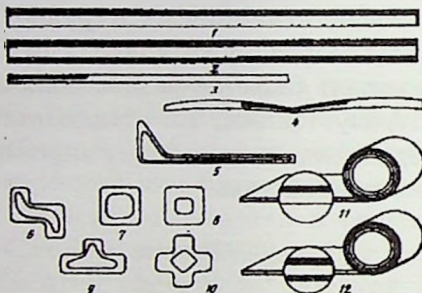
Поперечные сечения профилей сварных конструкций:
